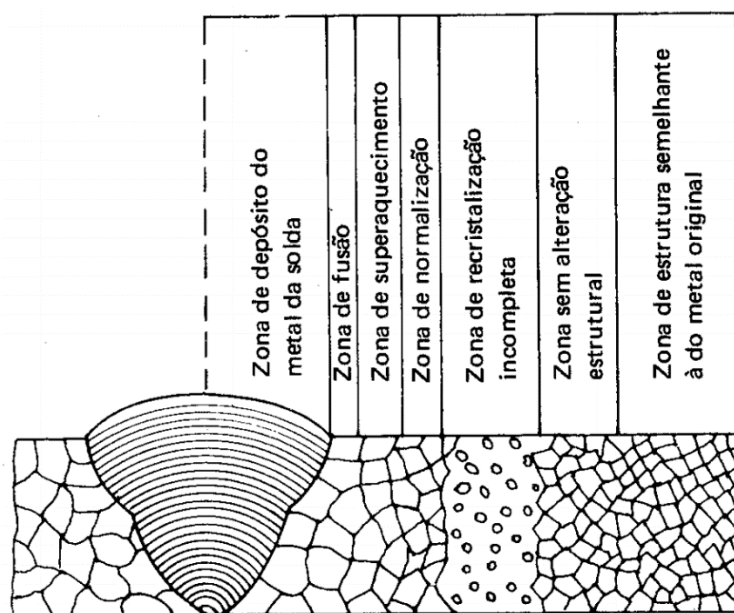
Representação esquemática dos fenómenos metalúrgicos que ocorrem na soldadura de um aço [27]
